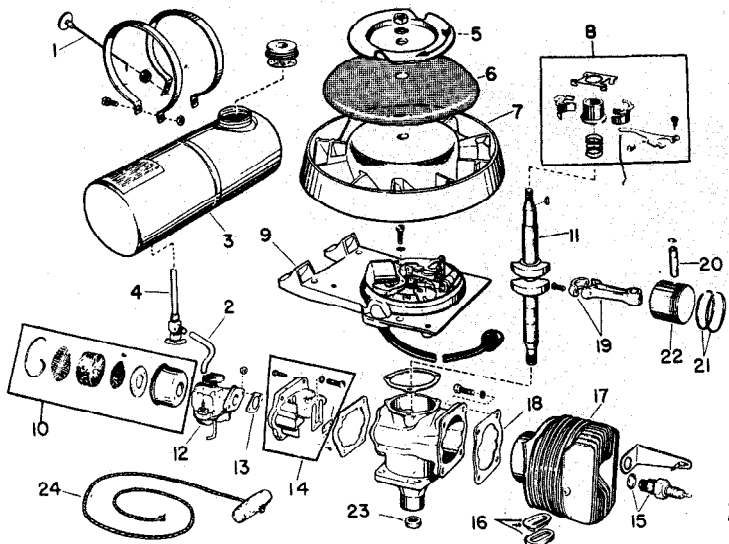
Despiece de un motor monocilindrico refrigerado por aire utilizado en una cortadora de césped (Lawnboy Division of Outboard Marine Corporation).
